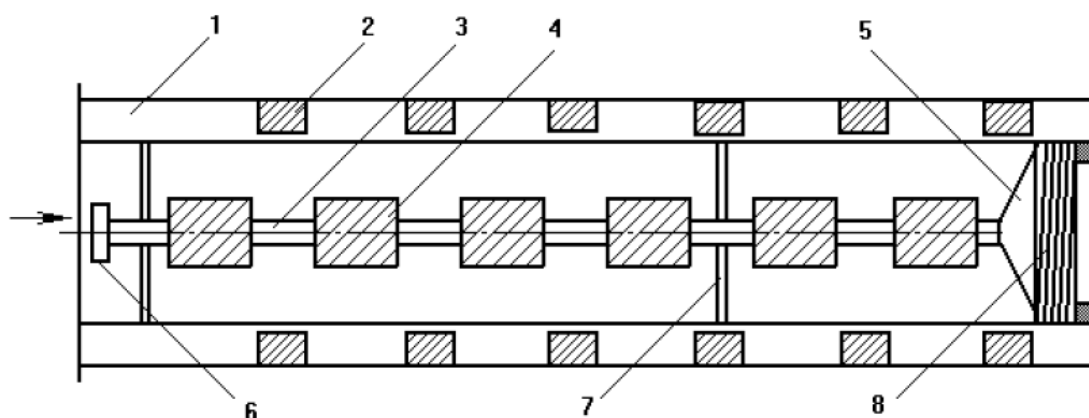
Электромагнитное устройство для обработки жидкости [59]: 1 - цилиндрический корпус из диамагнитного материала, 2 - кольцевая магнитная система, 3 - сердечник, размещенный в корпусе
